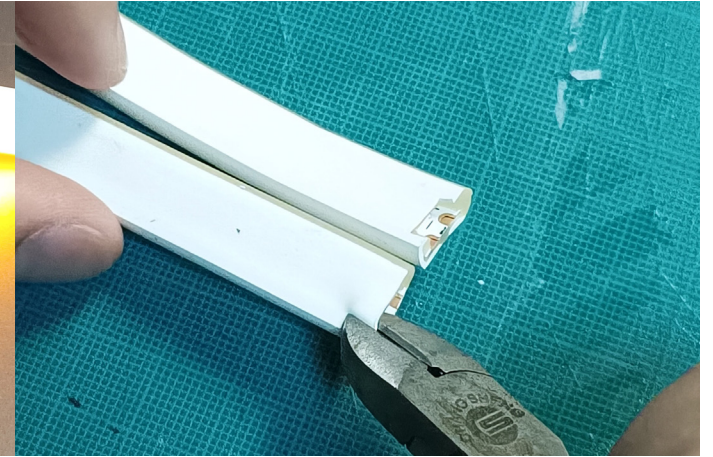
Per a facilitar les soldadures, amb unes tisores afilades o unes alicates de tall, tallarem un trosset del plàstic protector.
